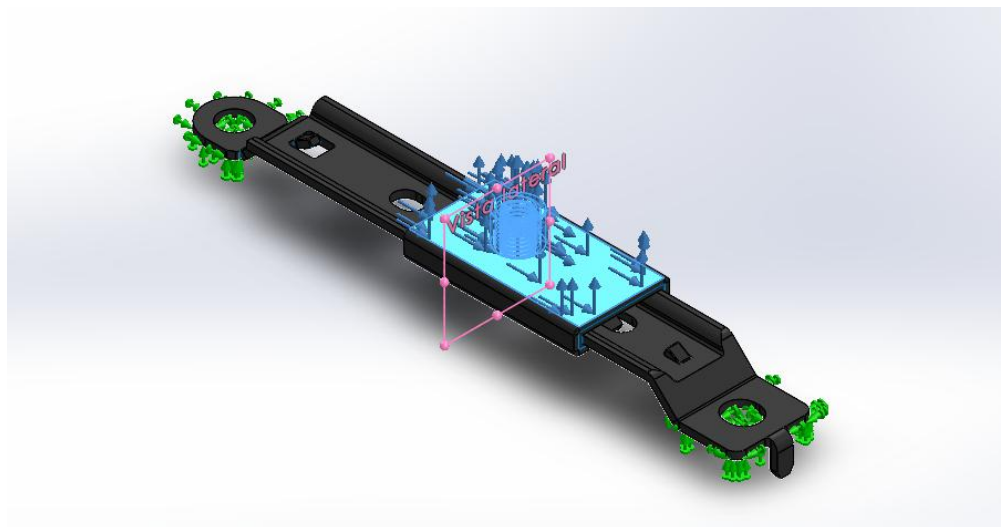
Vista de alzado del escenario 3D. Fuente: Autor
